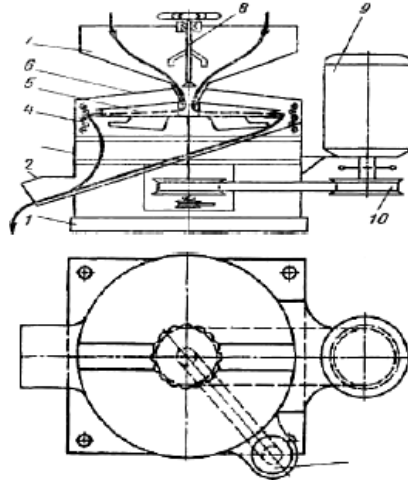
Схема скарифкатора СКС-1: 1 – станина; 2 – мішкотримач; 3 – корпус; 4 – обичайка; 5 – ротор - вентилятор; 6 – кришка; 7 – засипний ківш; 8 - регулюючий запірний конус; 9 – електродвигун; 10 – варіатор; 11 – тахометр.
